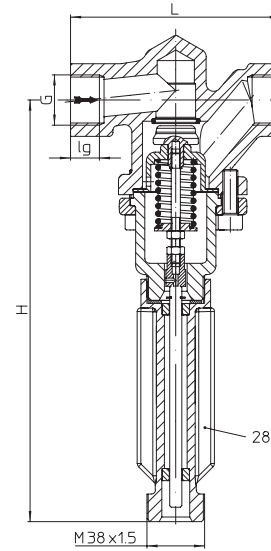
2..1 soğutma parçası ile maks. 250°C
